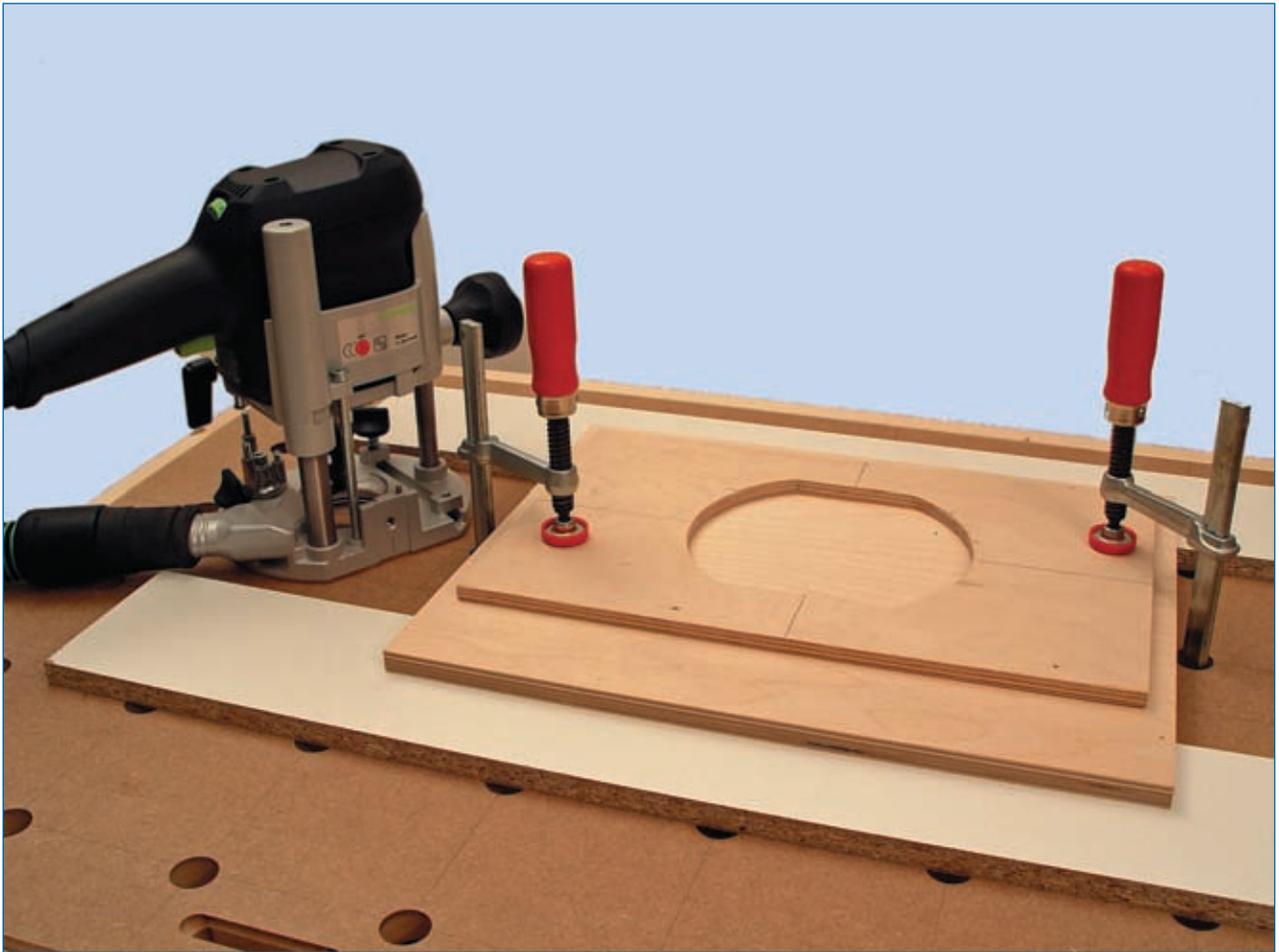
Auch runde Werkstücke sind auf einem solchen Tisch sicher zu befestigen.
